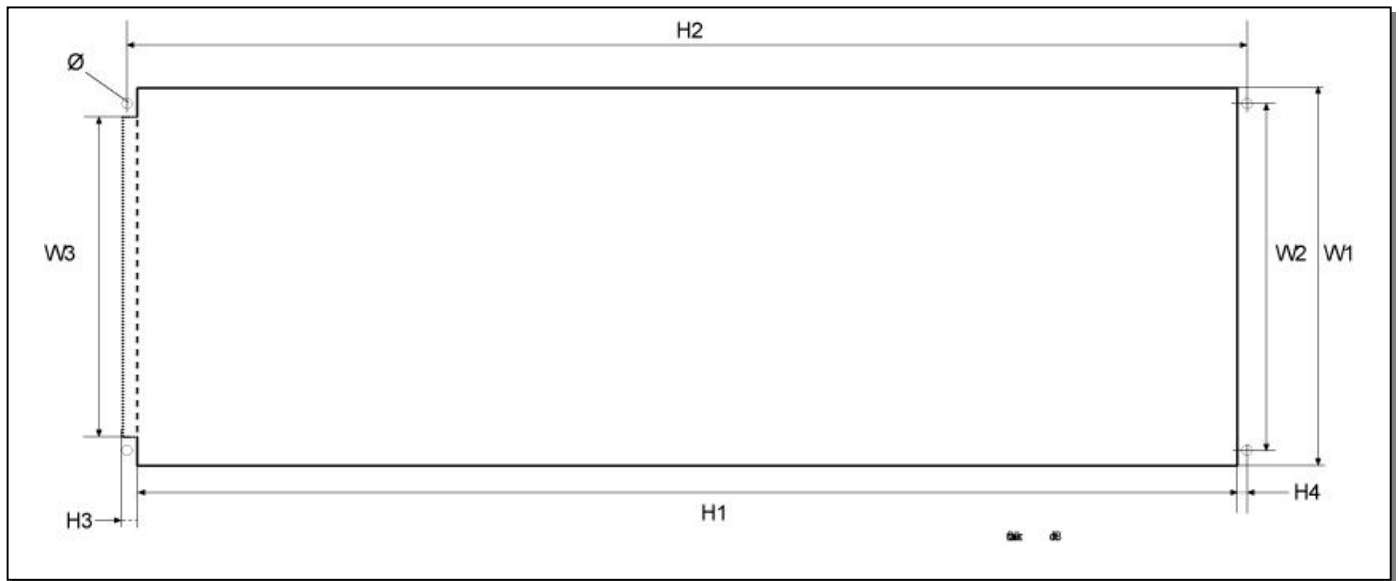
Orificiul necesar pentru montare cu flanșă, de la FR4 la FR6
